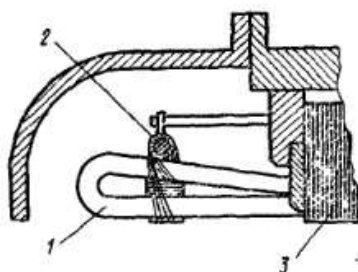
Крепление лобовых частей обмотки статора бандажными кольцами:
